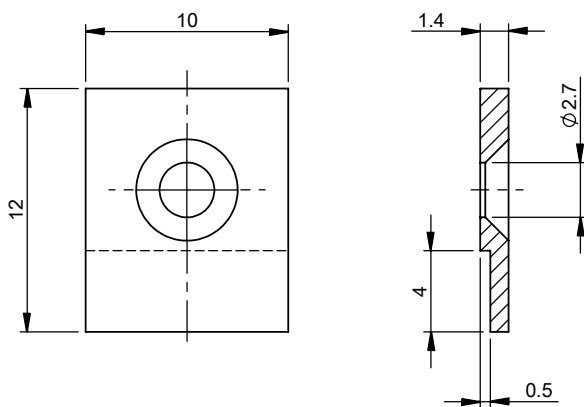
Retenedor BAM MC-ML-062-001-4
